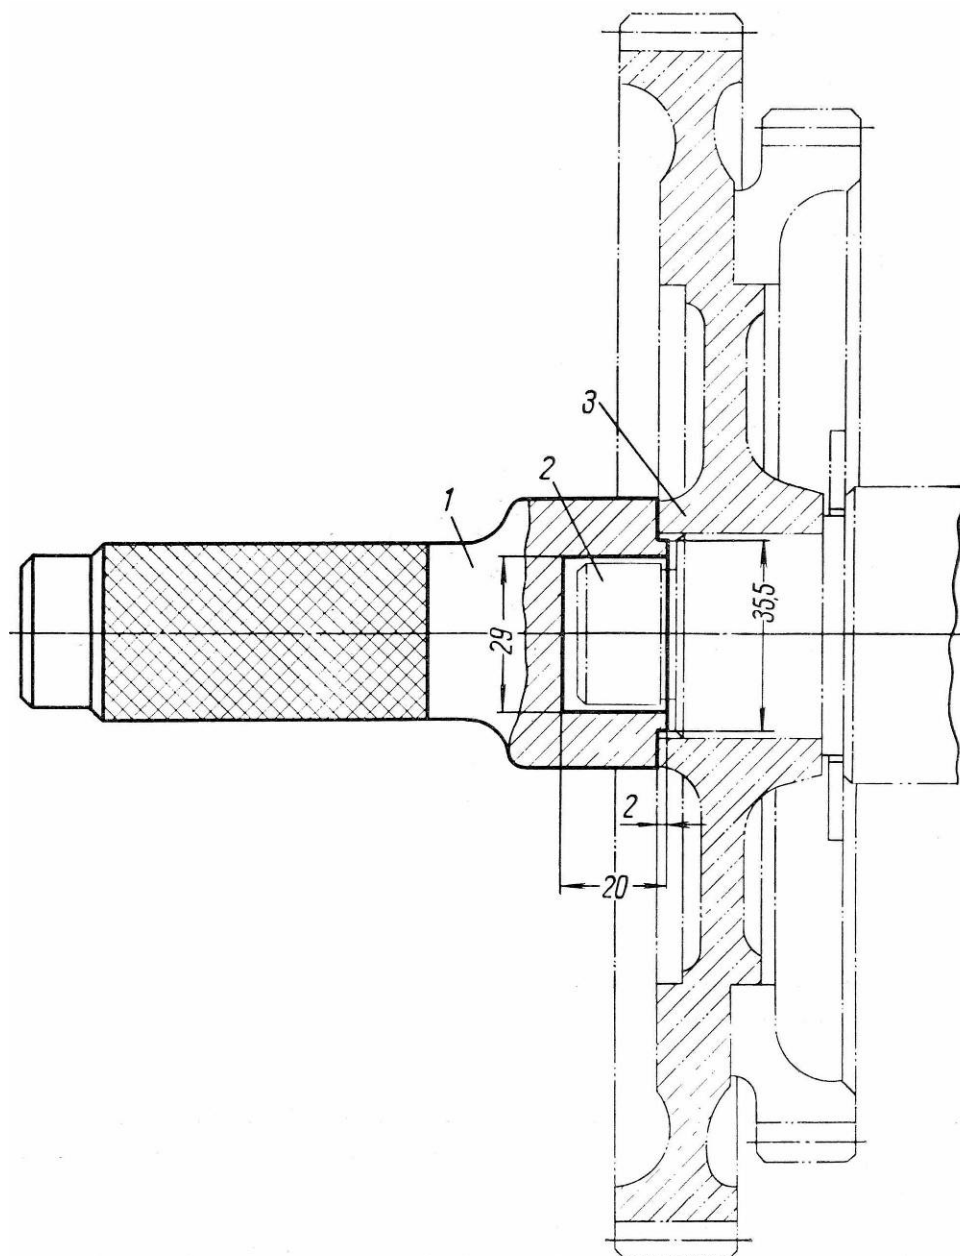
Оправка для напрессовки шестерни распределительного вала
